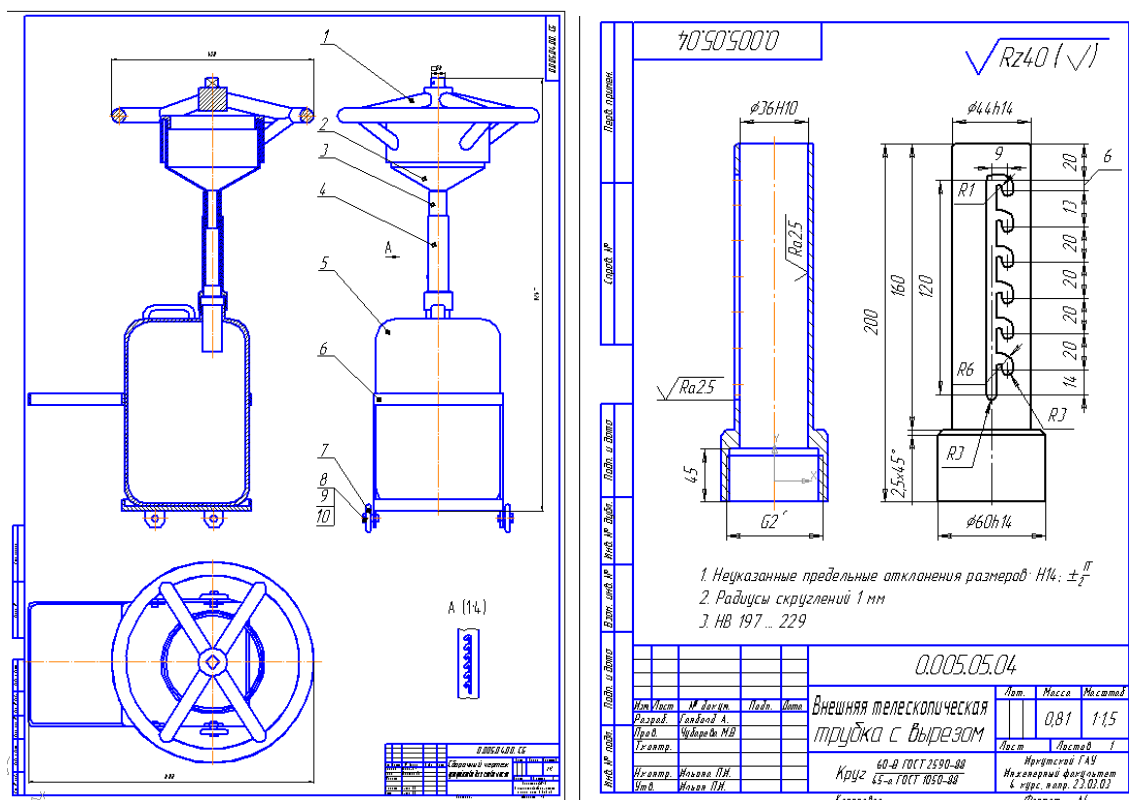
Сборочный чертеж установки для слива масла и детализовка телескопической трубки
